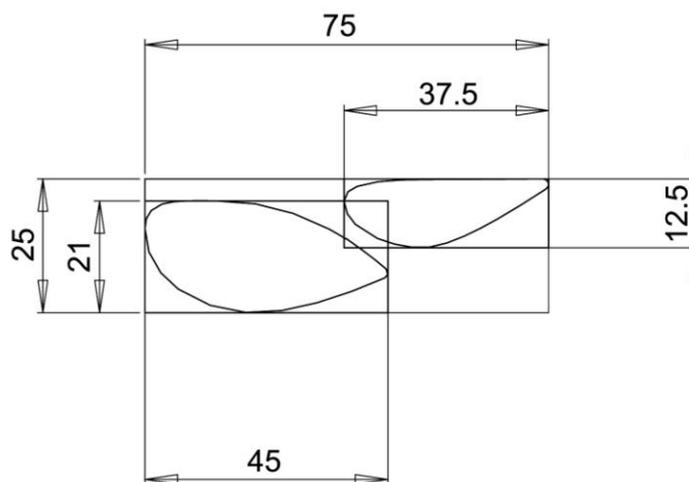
Ejemplo conforme de sección de un elemento formado por dos tubos (sección mínima de 1 cm aplicado a la horquilla, los cables y los soportes)
